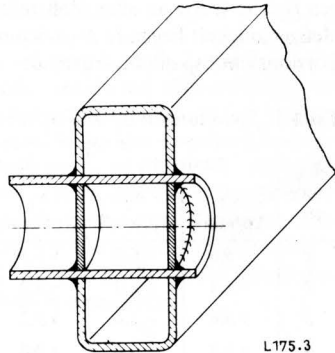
Durch eingeschweißte Ronden wiederhergestellter Rohrquerschnitt (nur möglich für den Zweck der Untersuchung mit Querträgerstumpf).
